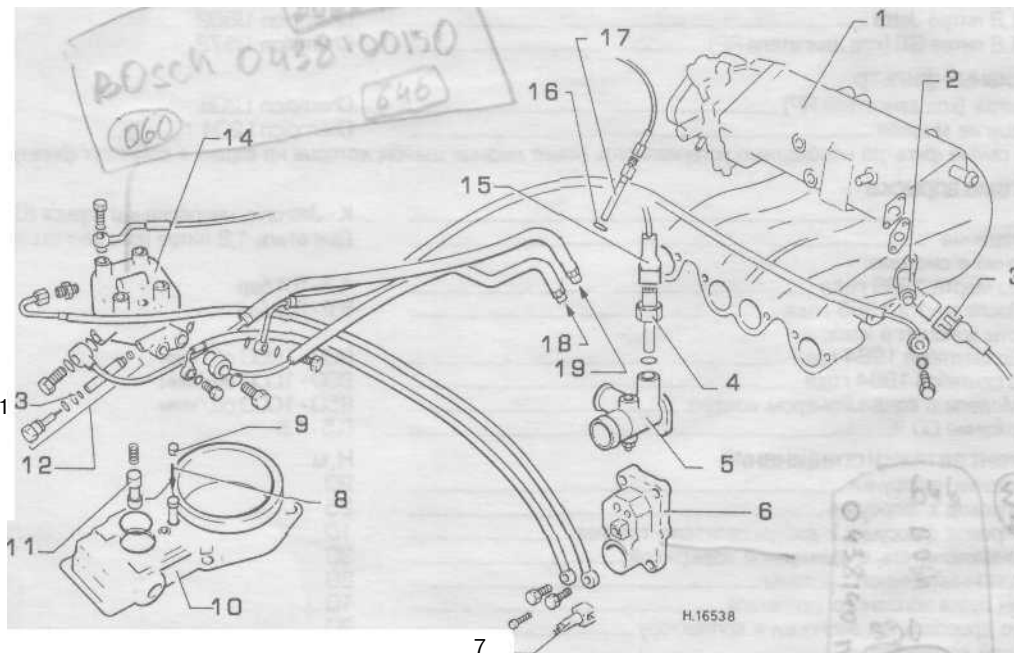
Детали подачи воздуха в системе впрыска топлива К - Jetronic - В клапанные двигатели
